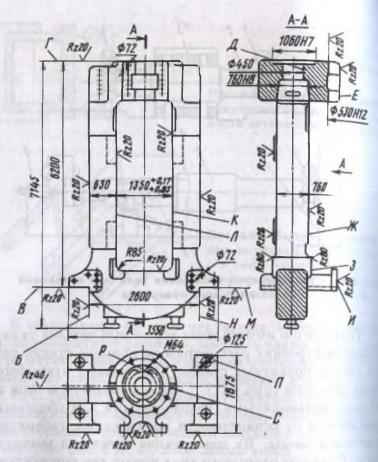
Станина рабочей клети прокатного стана закрытого типа
